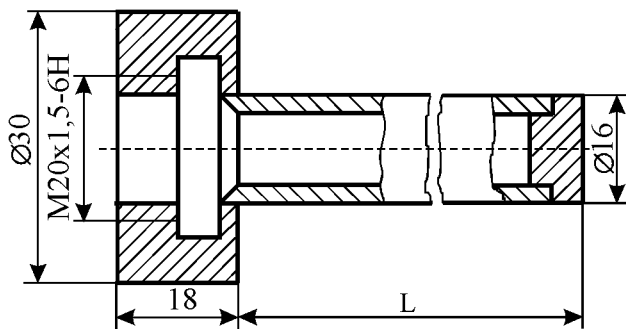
Габаритные и установочные размеры измерительного блока
